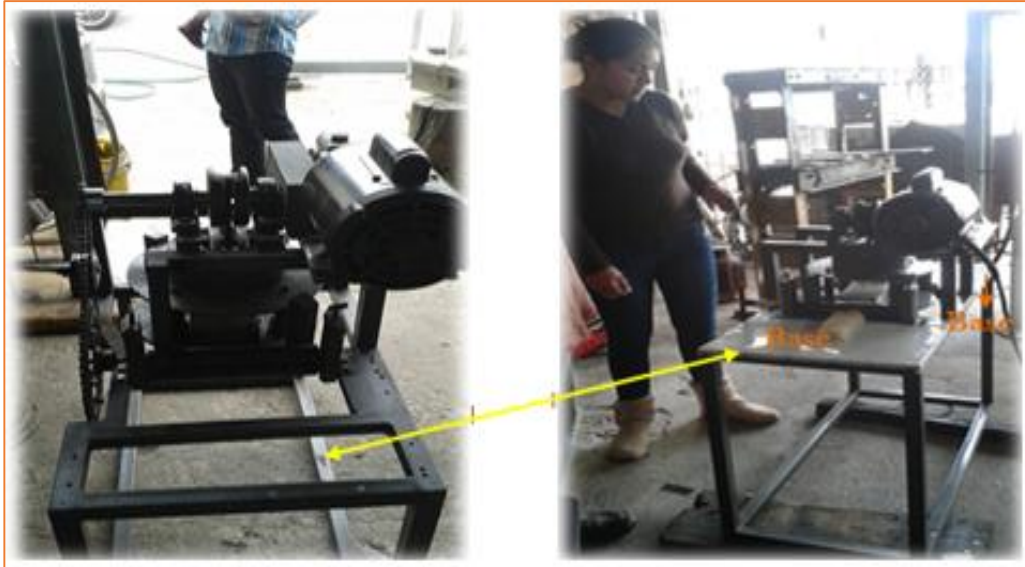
Montaje de las Bases a la Estructura Principal
